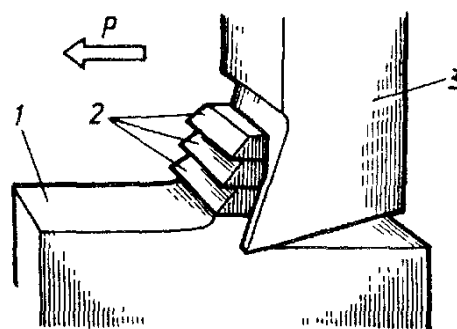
Процес утворення стружки: 1 - заготовка, 2 - стружка, 3 - різець
